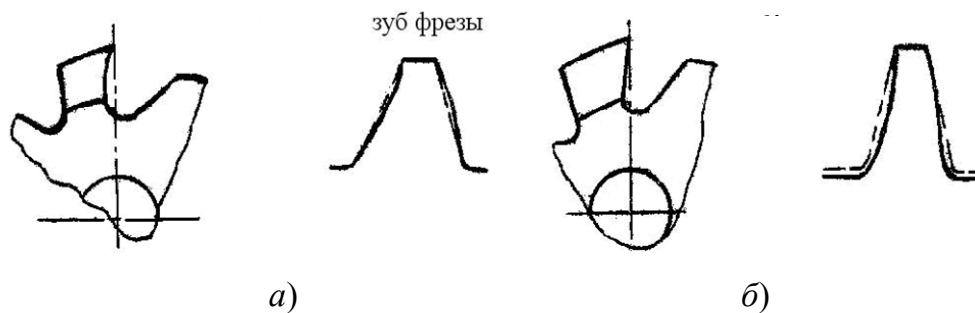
Фрезы передней поверхности зуба фрезы:
